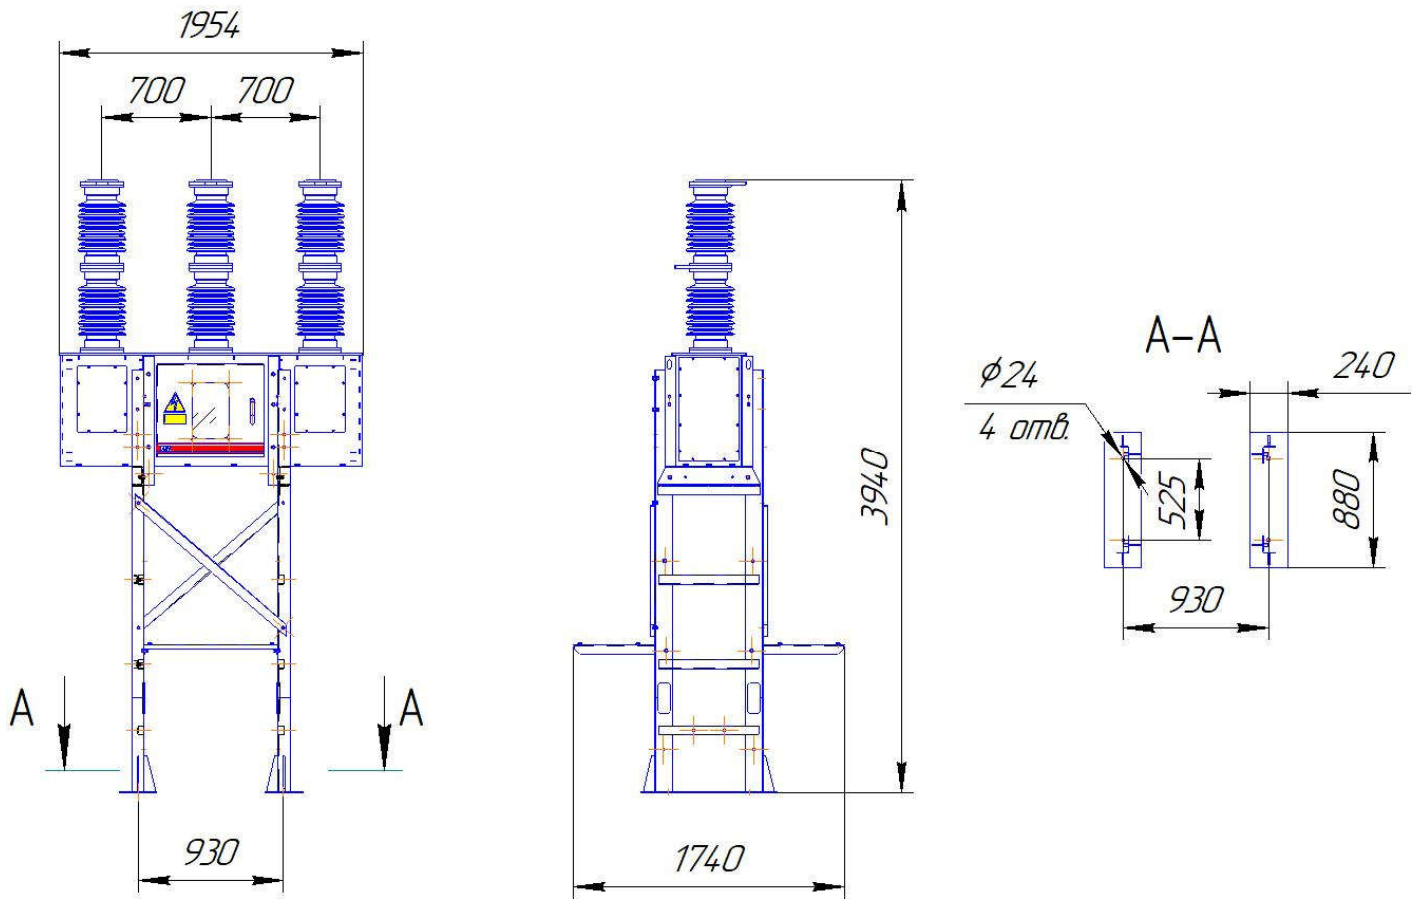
Габаритные размеры выключателя на опорной раме.
